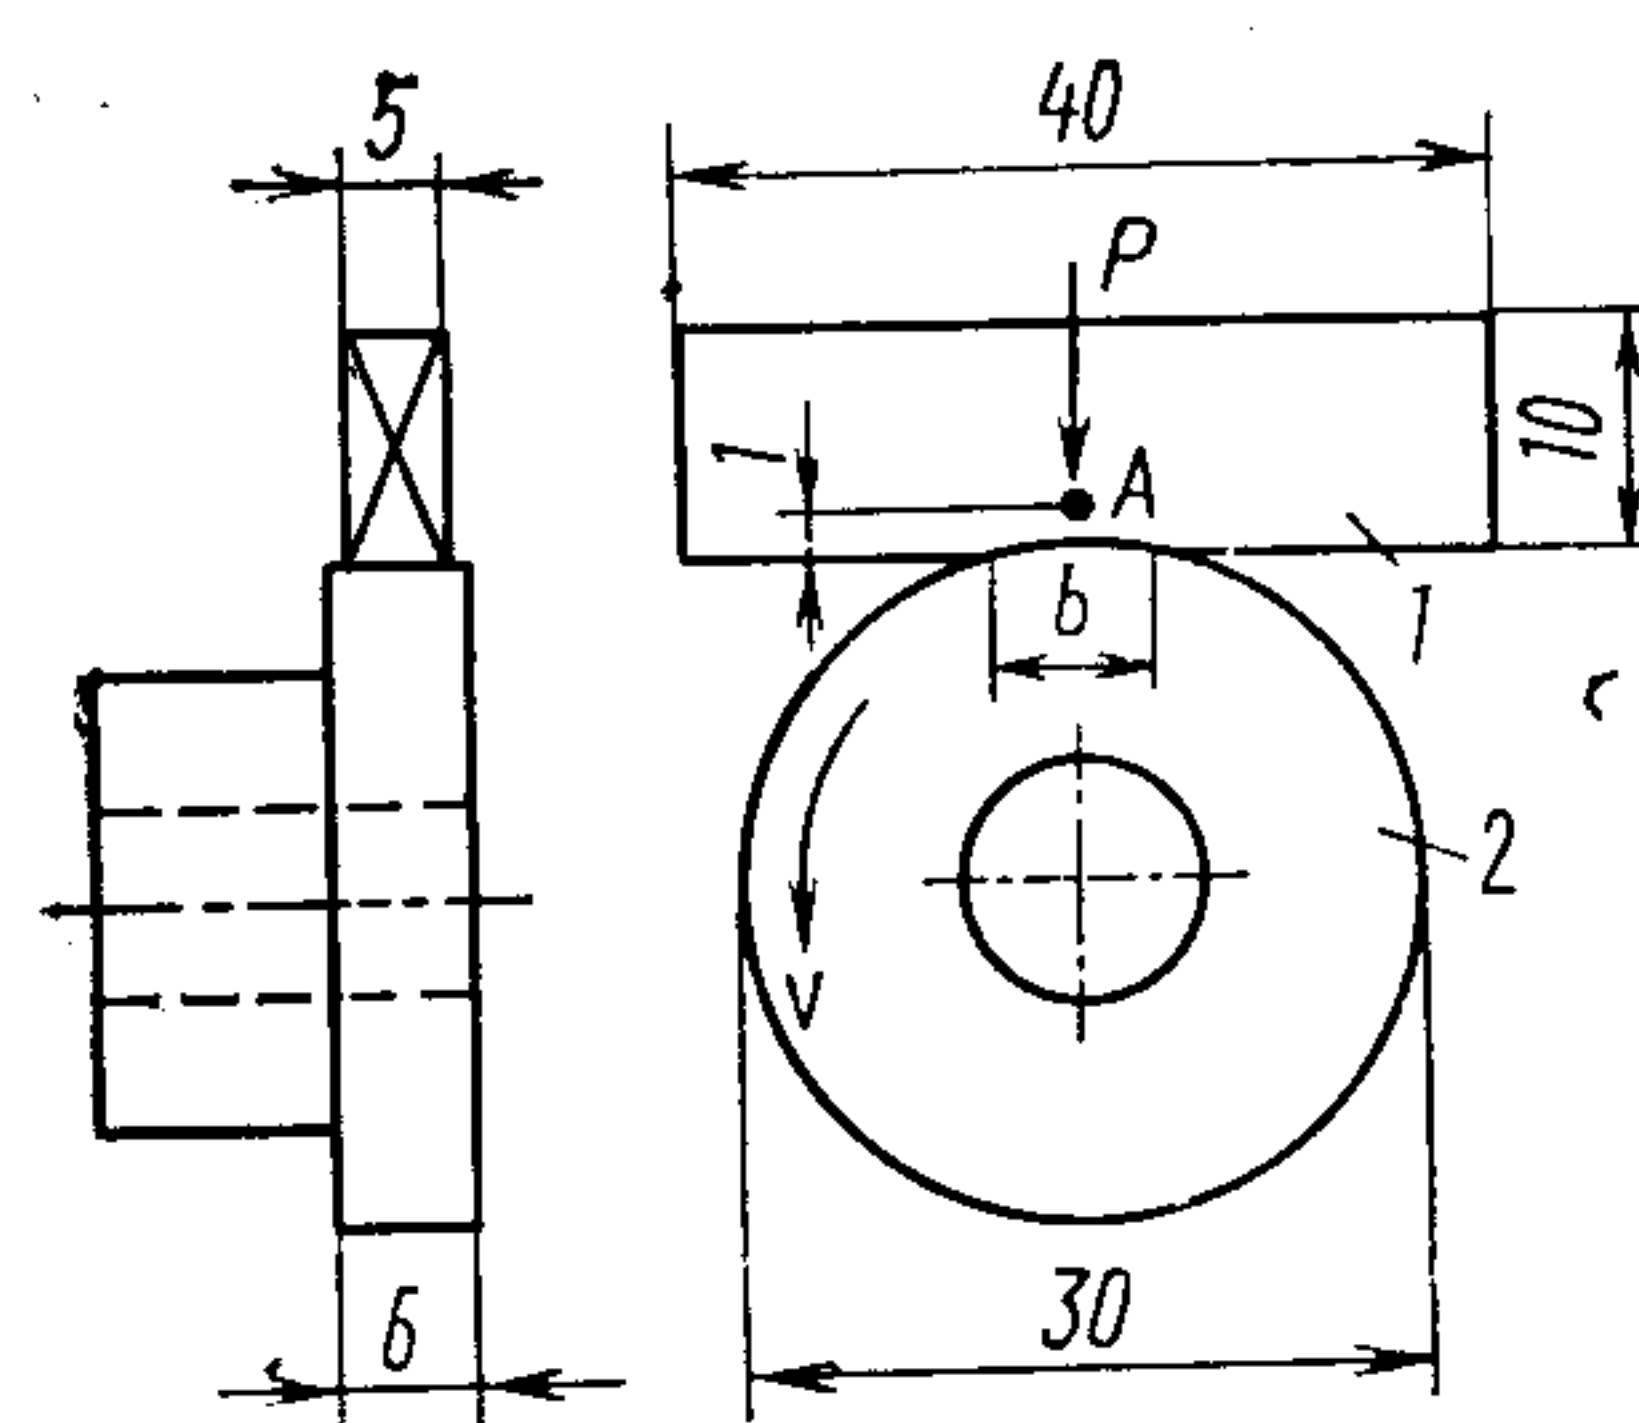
Эскиз образцов для испытаний на изнашивание при трении: 1 — пластинчатый образец; 2 — вращающийся диск
